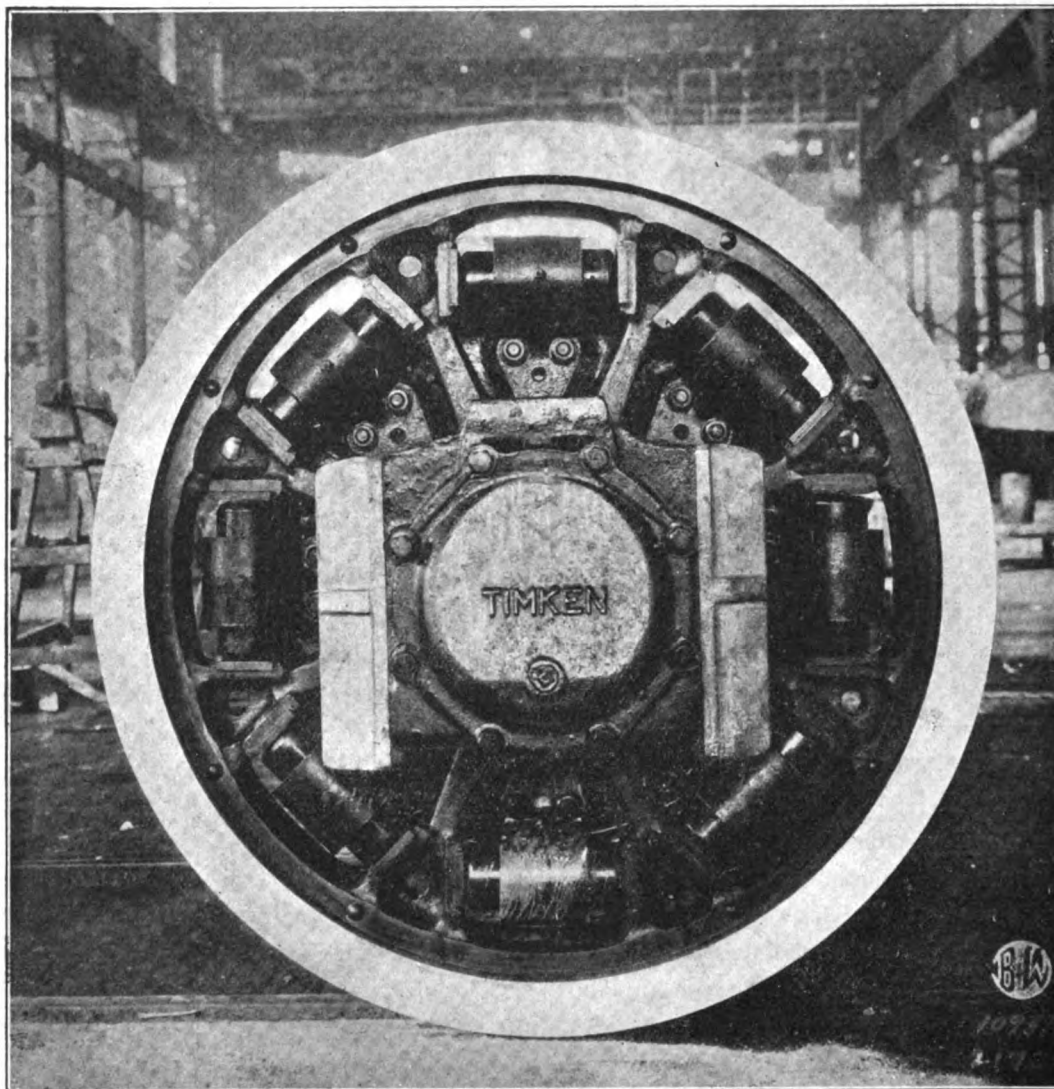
Asse motore con meccanismo « quill cup drive » dei locomotori per espressi tipo pesante 2-C<sub>0</sub>-2, serie P-5, 470 della « Pennsylvania Railroad ».
